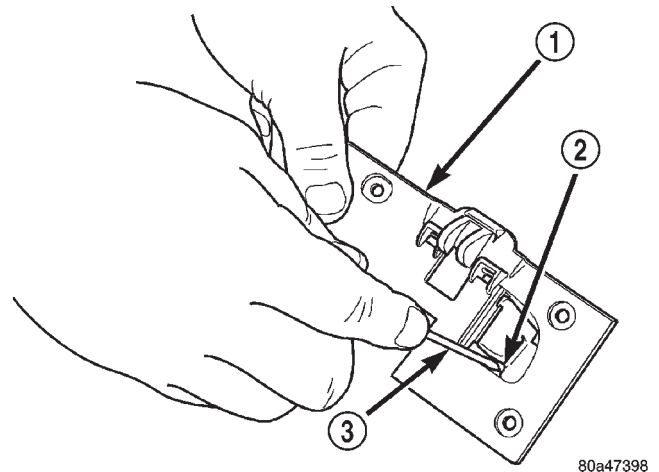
Desmontaje e instalación del cilindro de cerradura de la guantera
